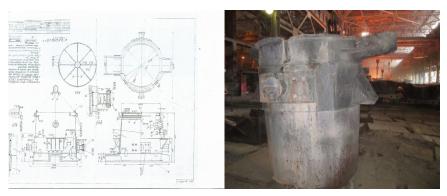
Сборочный чертеж и общий вид разливочного ковша ПЦ-1
